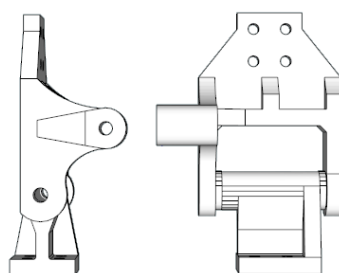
Вид сбоку и сверху шарнирного соединения
